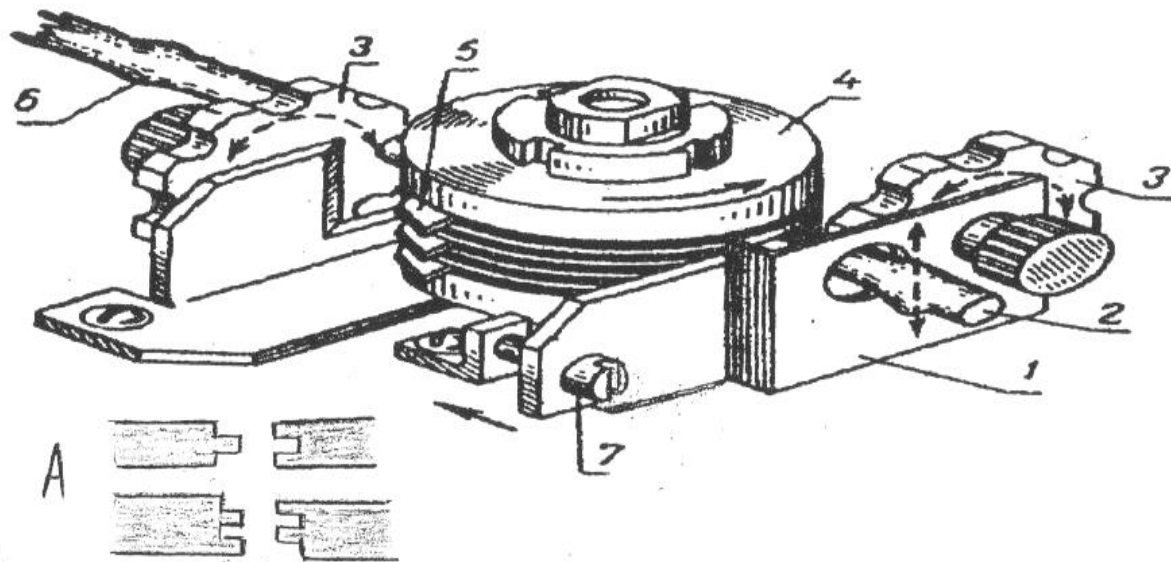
Рабочий узел прививочной машины МП-7: 1— Защитный щиток; 2 — черенок привоя; 3 — опорный круг; 4 —режущая головка с ножами (5); 6 — подвой; 7 — регулировочный винт соостности срезов. А – виды выполненных срезов
